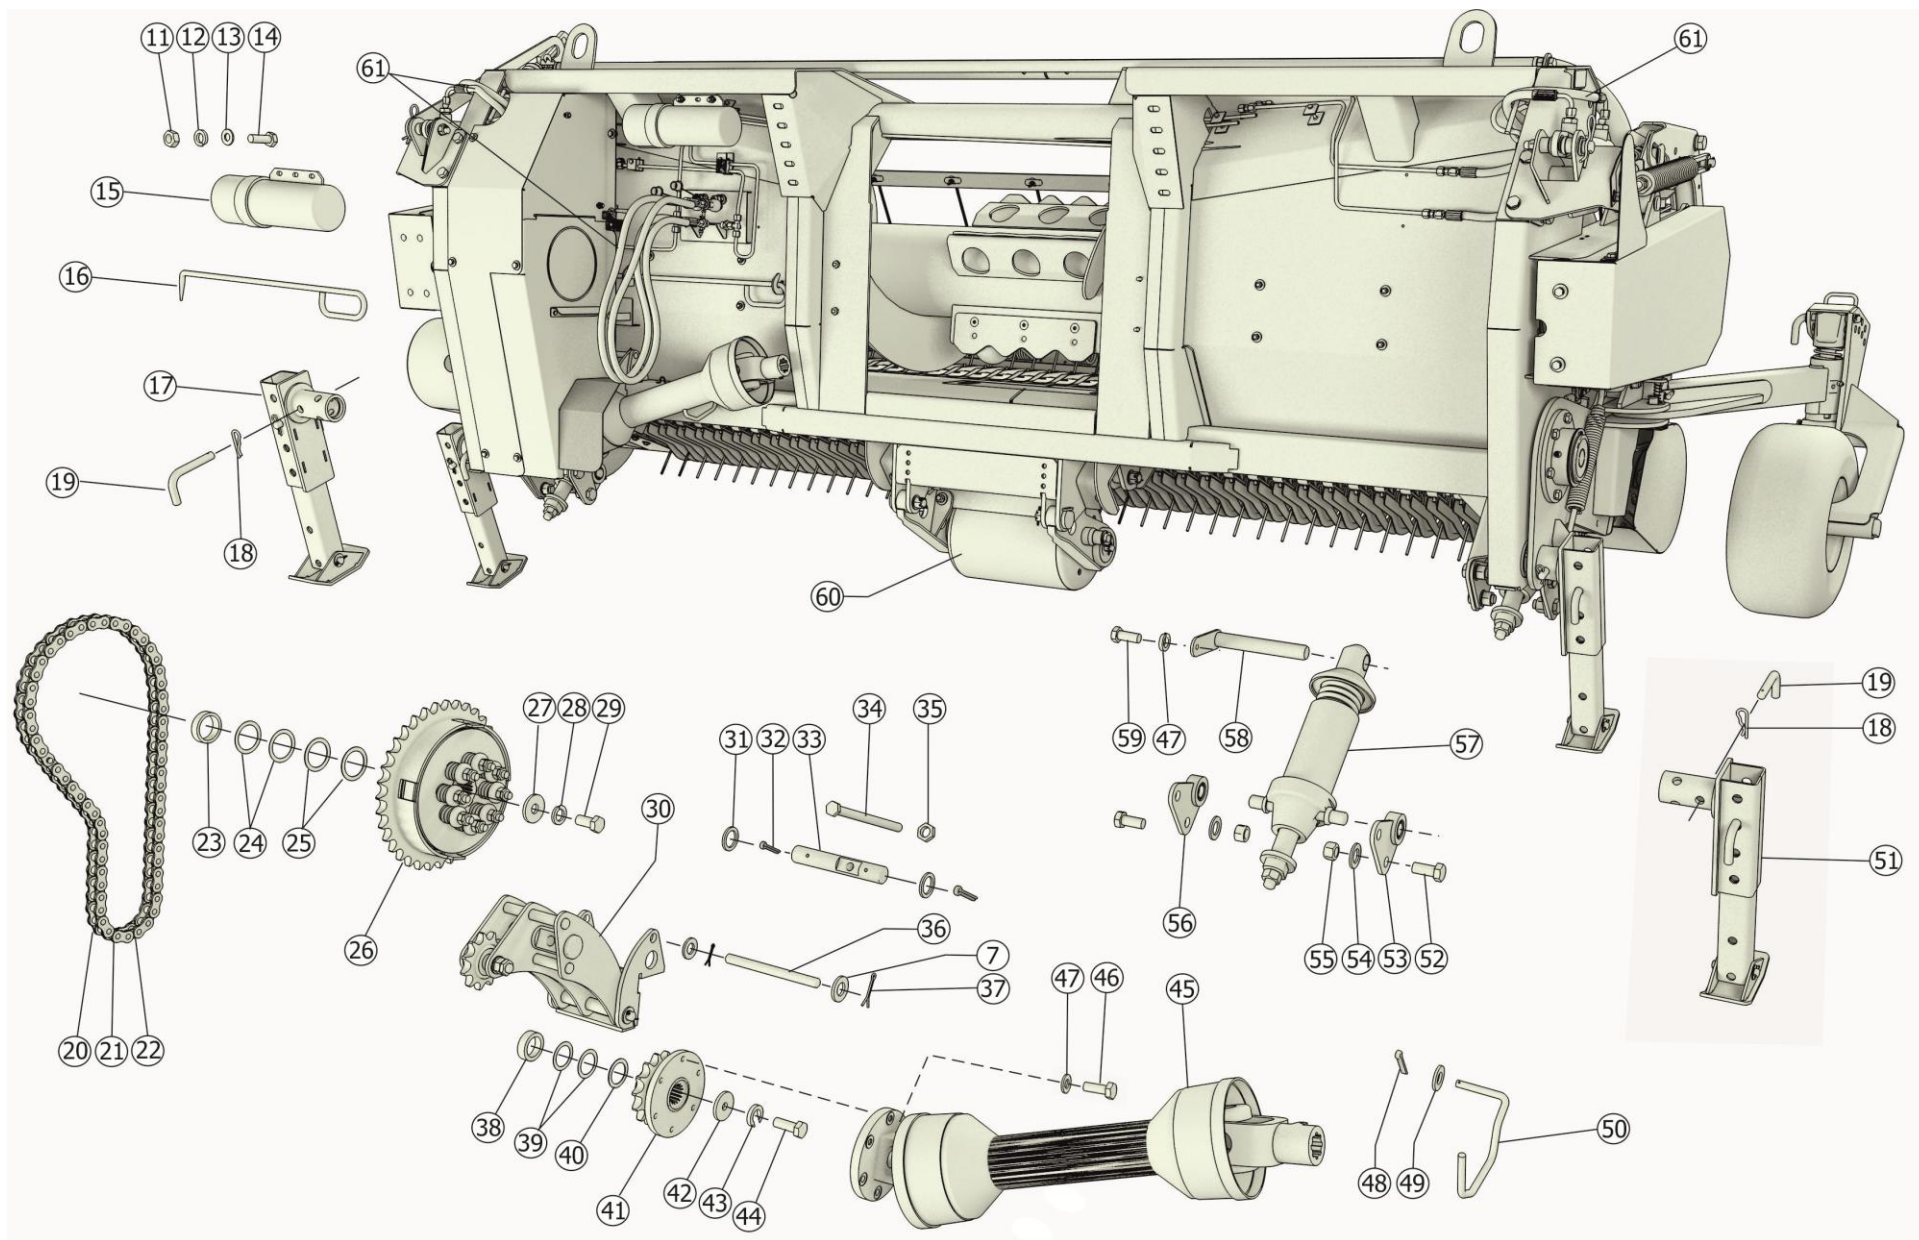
Подборщик кормоуборочный ПК-300.01.00.000Г. Общий вид
